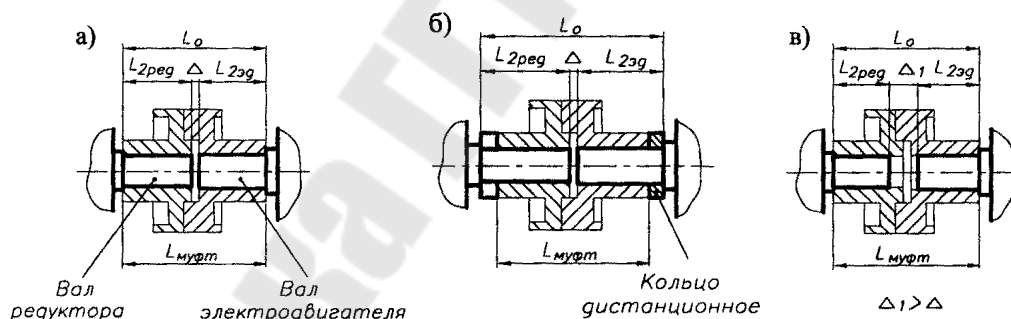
Варианты соединения валов электродвигателя и редуктора
